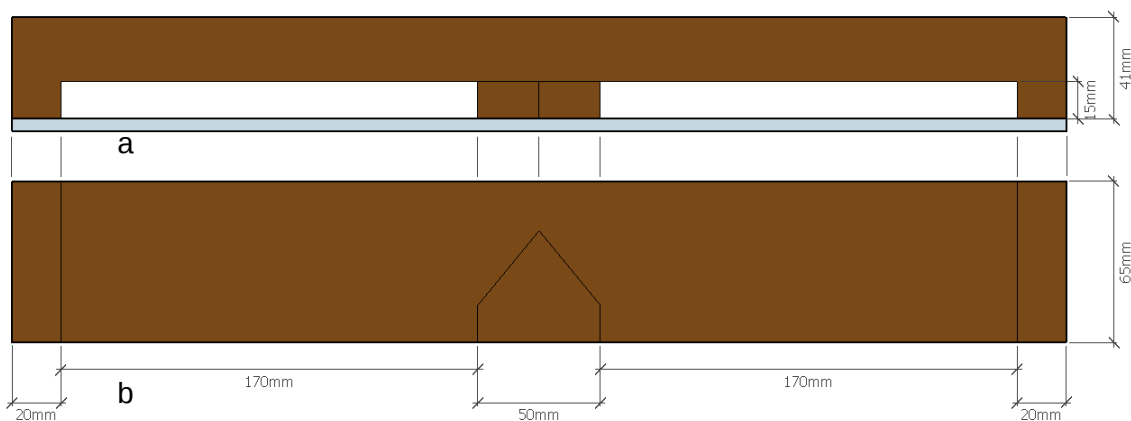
Esquema e medidas da estrutura da área de monitorização: (a) vista frontal (vista do exterior para o interior da colmeia) e (b) vista de base (a quilha aponta para o exterior)
